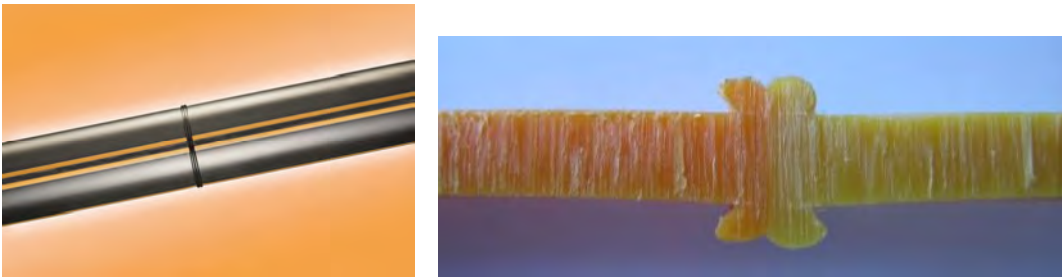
Stumpf-/Spiegel-Schweißung; Rechts: Querschnitt durch die Schweißnaht (Bruckner, 2015).
